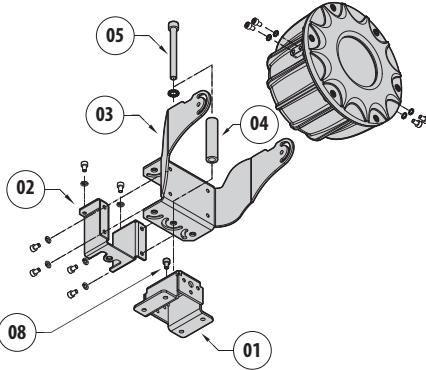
Fixation sur parapet avec entrée des câbles dirigée vers le haut.
